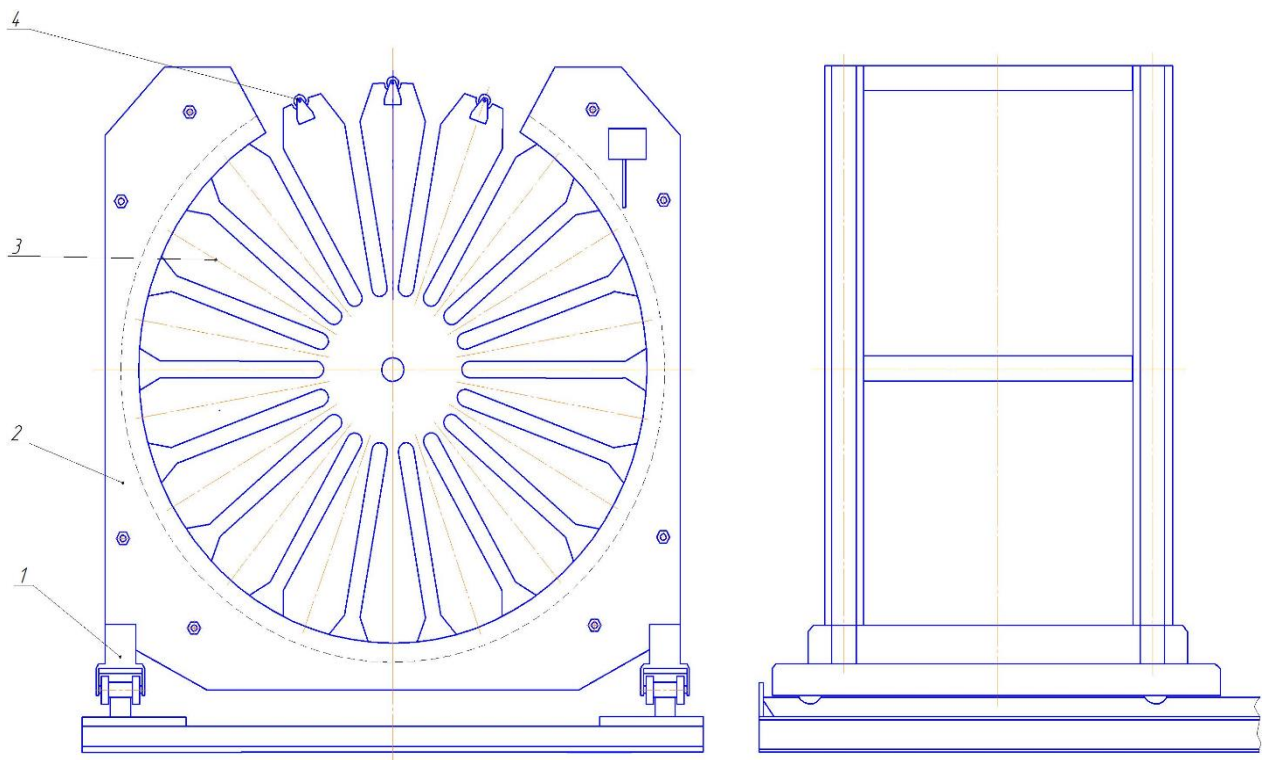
Схематичне зображення візка подачі арматурних прутків:
